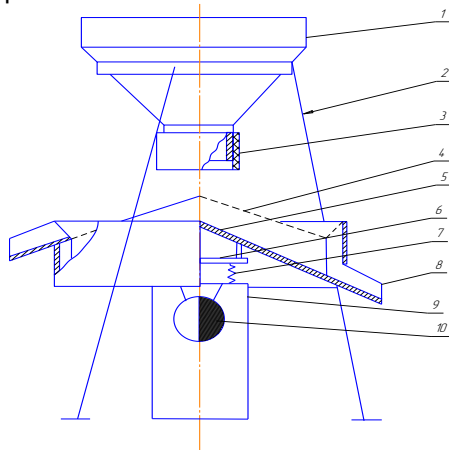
Схема віброгрохоту з конічною ситовою поверхнею: 1 – бункер; 2 – опора; 3 – заслінка; 4 – сито; 5 – скатний конус; 6 – віброплатформа; 7 – пружний елемент; 8 – вивантажувальний лоток; 9 – станина; 10 – віброзбуджувач.
